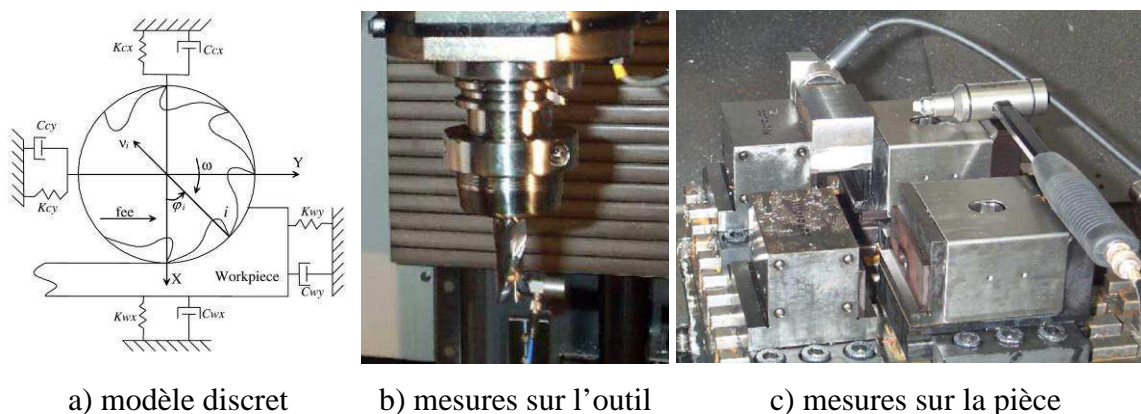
Modèle de l'ensemble machine - outil – pièce et son identification
